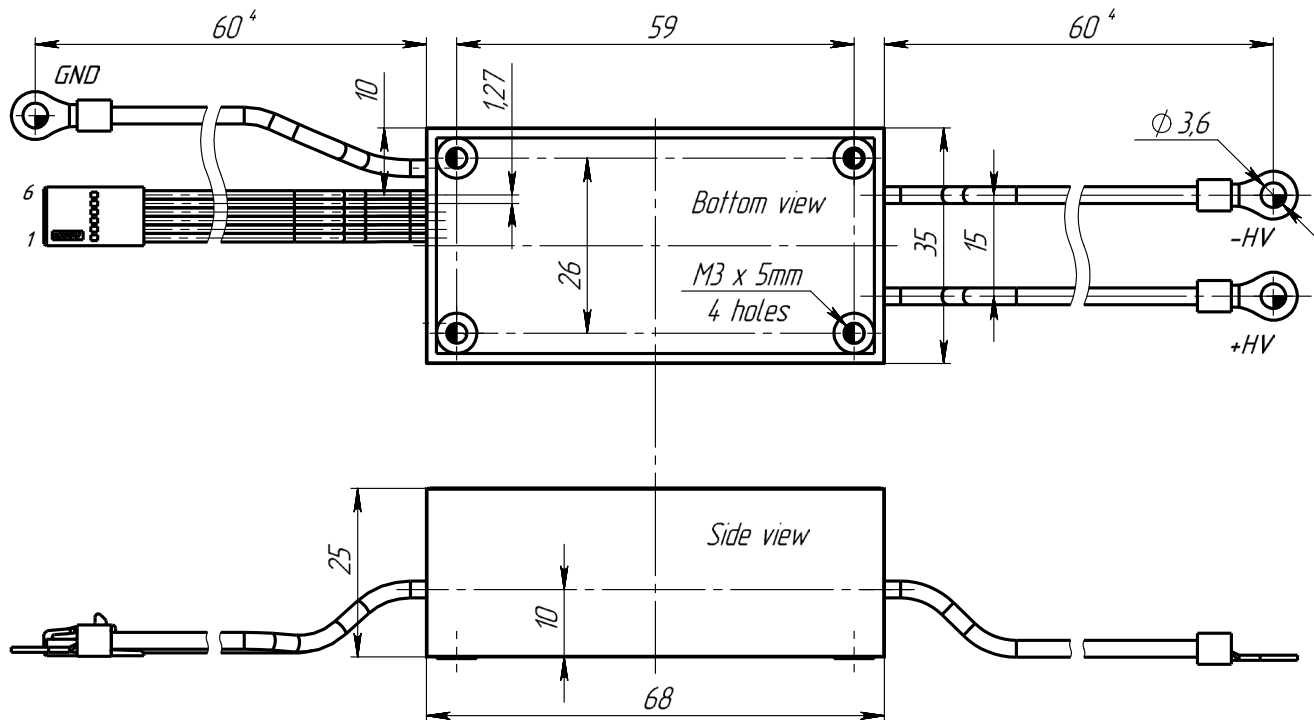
Чертеж и внешний вид коммутатора серии HVS-B1 в пластиковом корпусе для крепления на раму
